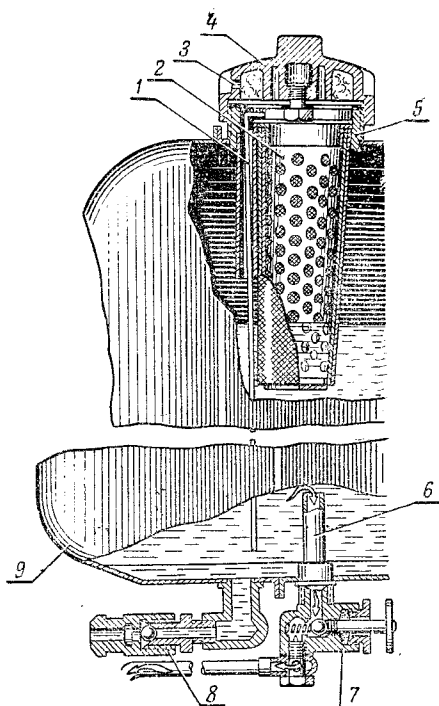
Топливный бак трактора ДТ-75: 1—линейка для замера уровня топлива; 2—сетчатый фильтр; 3—отверстие для сообщения полости бака с атмосферой; 4—крышка наливной горловины; 5—наливная горловина; 6—трубка; 7—расходный кран; 8—сливной кран; 9—корпус.
